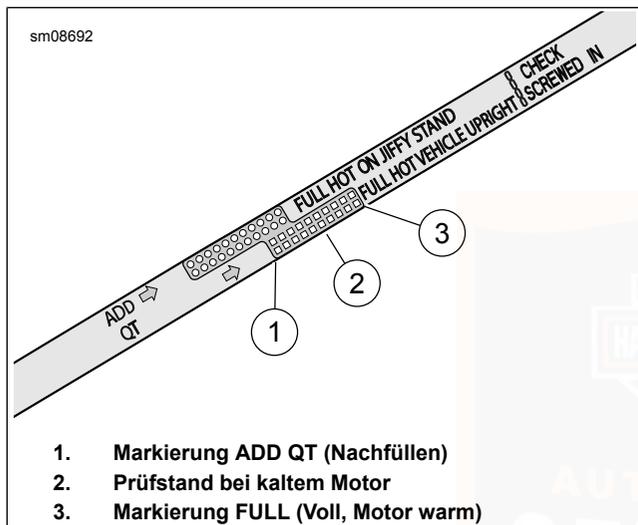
Motor-Ölmesstab (Anzeige VEHICLE UPRIGHT [Fahrzeug aufrecht])
